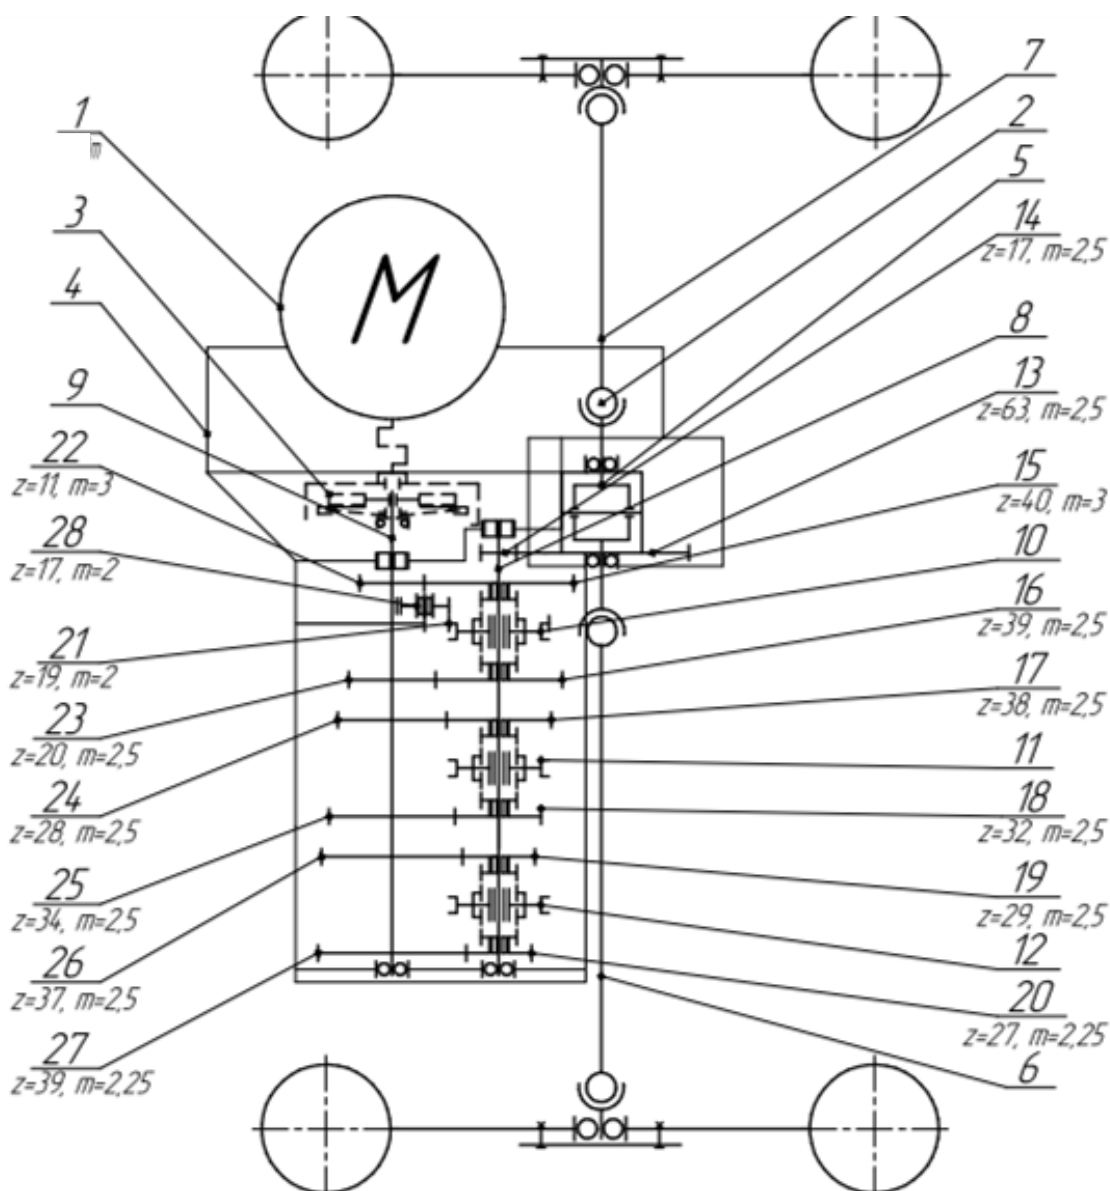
Кинематическая схема предлагаемой конструкции
